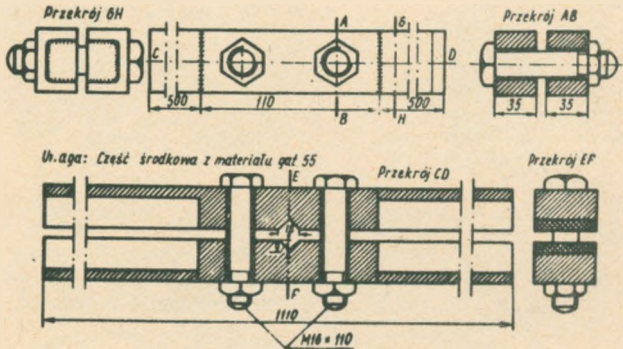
Zakończenie pierwszego pręta przy wbijaniu ręcznym
